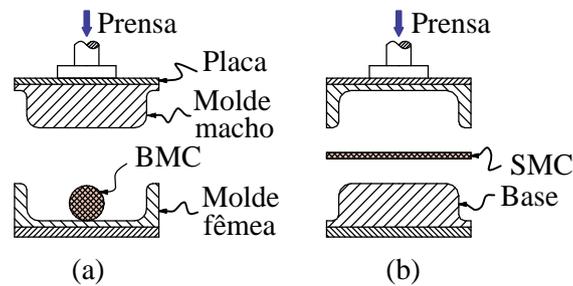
Moldagem por compressão usando bloco (BMC) e chapa (SMC) preformados, nas figuras (a) e (b) respectivamente, em moldes de encaixe.
